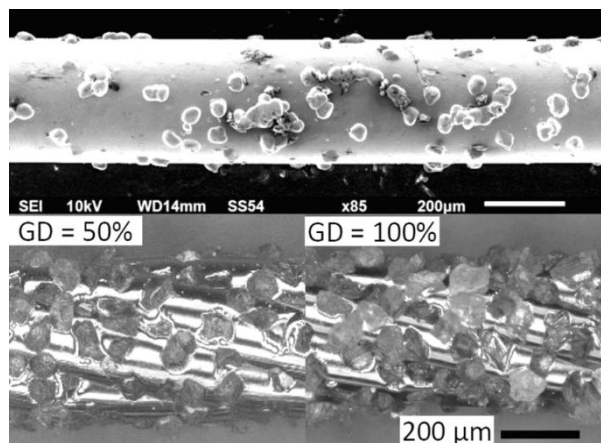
Зверху: звичайний різальний інструмент для обробки кремнію. Знизу: використаний різальний інструмент для обробки композиту [27]
